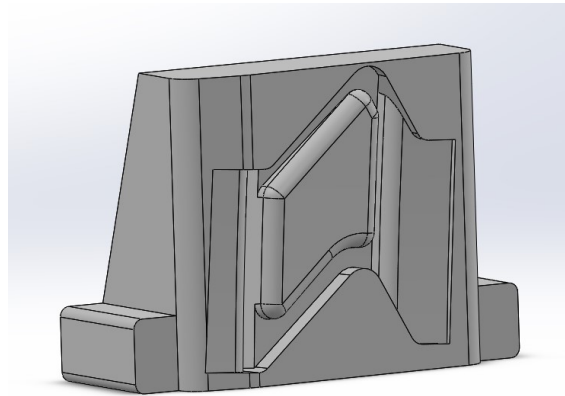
Macho desenvolvido para auxiliar extração da pá de turbina
